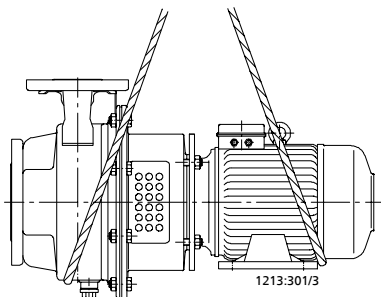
Транспортировка насосного агрегата с опорной лапой двигателя
